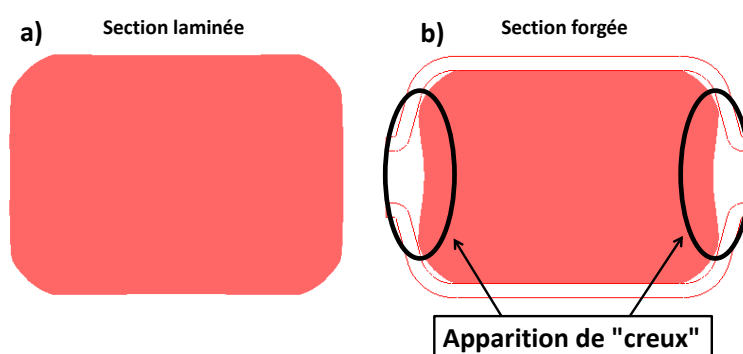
Aire a) de la barre après la cage 2 (31671mm^2) et b) du lopin après forgeage de la passe 2 (311mm^2)
